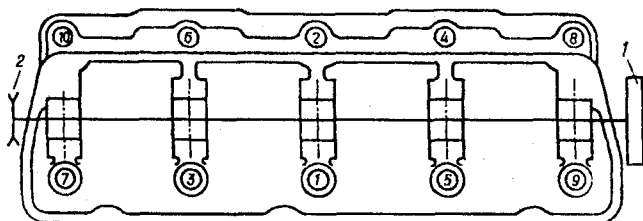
Схема затяжки болтов крепления головки цилиндров: 1 — маховик; 2 — ведомый шкив привода коленчатого вала
